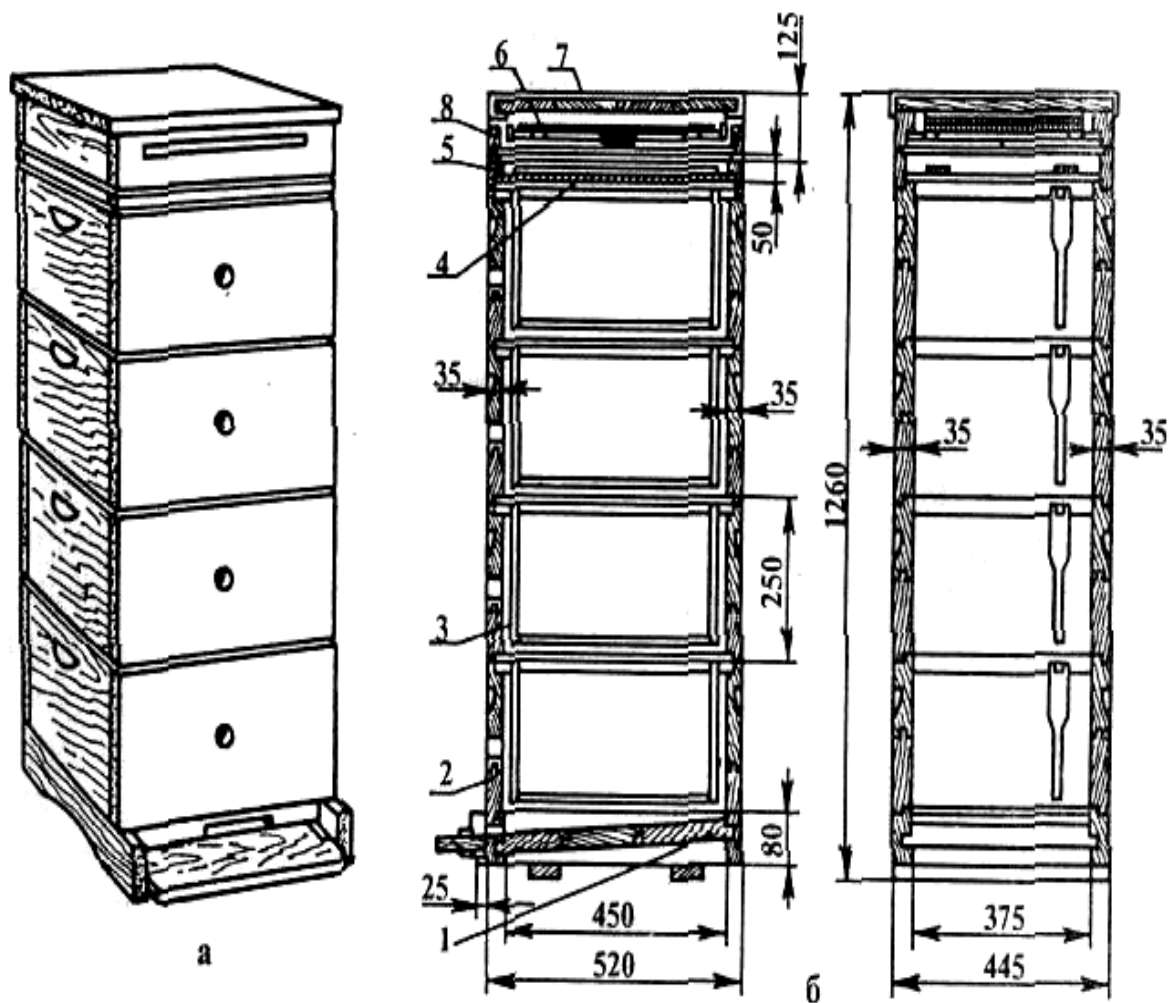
Многокорпусный улей: а - общий вид; б - устройство; 1 - дно; 2 - корпус; 3 - рамка; 4 - потолок; подкрышник; 6 - вентиляционная рама; 7 - кровля; 8 - обвязка крыши
